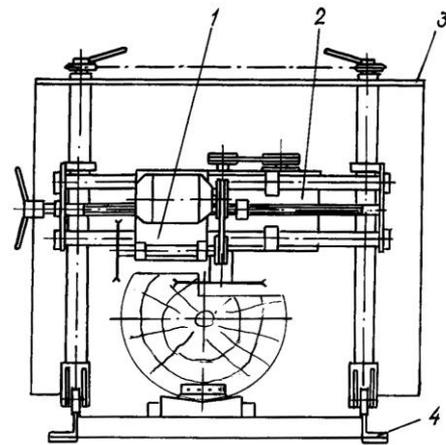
Схема лесопильной установки 2ЦДБ-60: 1 – суппорт отрезной пилы; 2 – суппорт делительной пилы; 3 – портал; 4 – рама с направляющими путями
